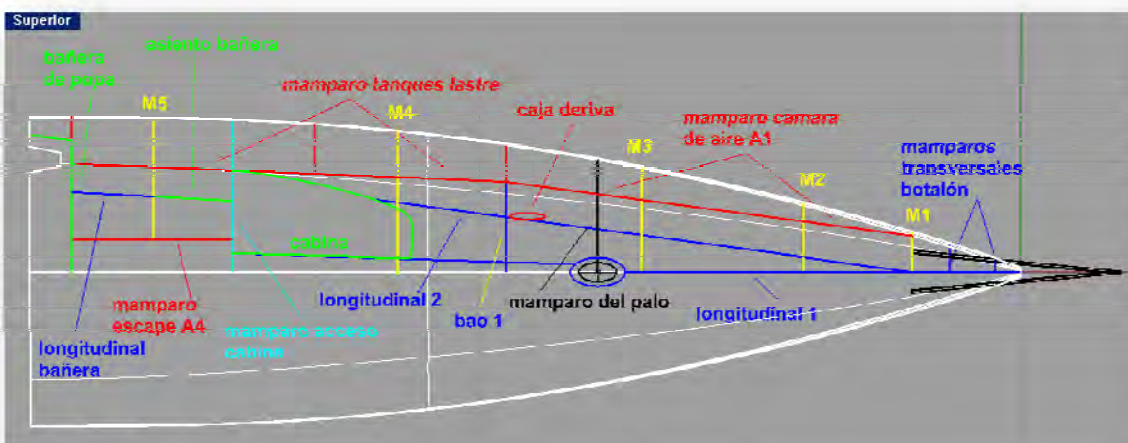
9. Disposición final de los refuerzos de la cubierta
